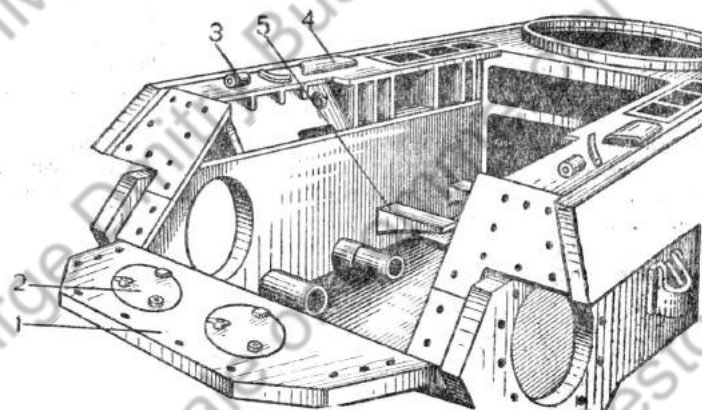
Корма корпуса; вид со стороны моторного и трансмиссионного отделений:
